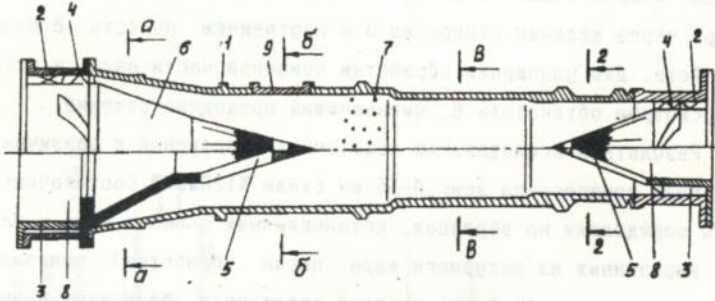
Схема установки для пневмоимпульсной обработки валов компрессора
